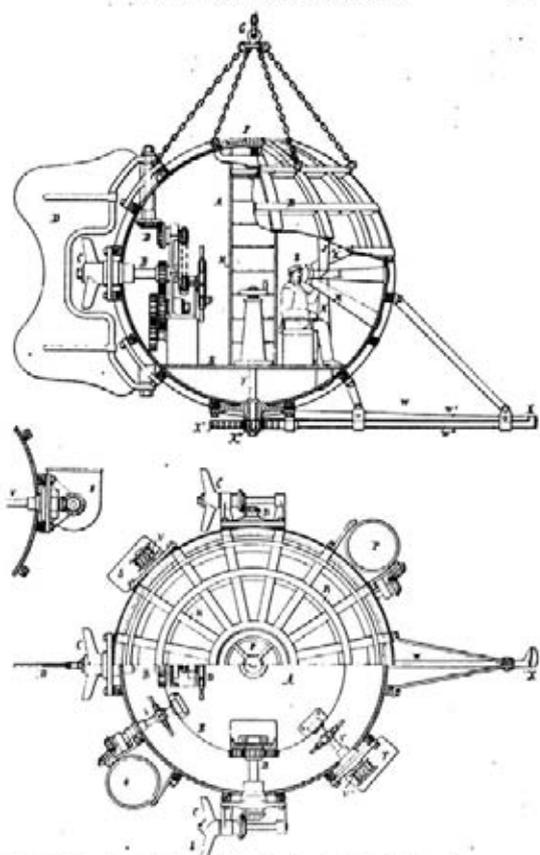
et 28. — Coupe verticale, dessin et dessin coupe horizontale de Transférer sous-marin
